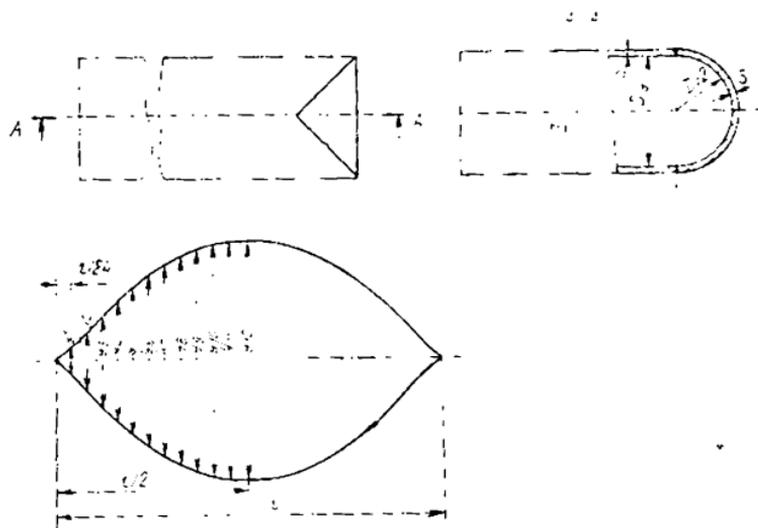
Заглушка цилиндрическая на  $p_y \leq 16 \cdot 10^5$  Па и шаблон для разметки заглушки
